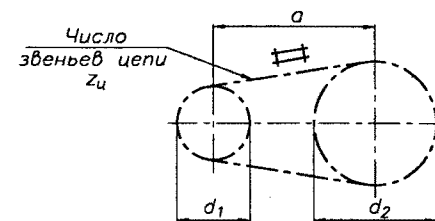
Схема и основные размеры передачи с приводной роликовой (втулочной) цепью
